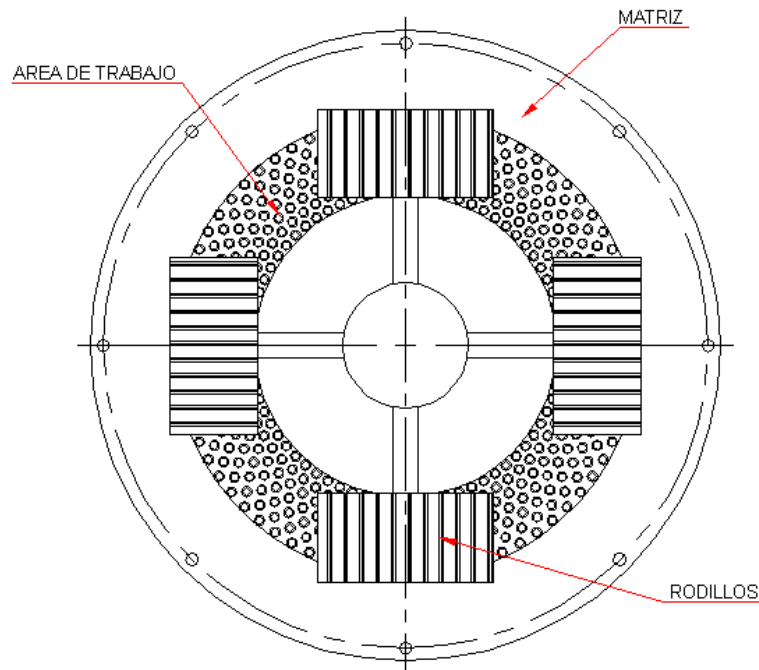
Esquema de los rodillos de compresión y matriz principal.
